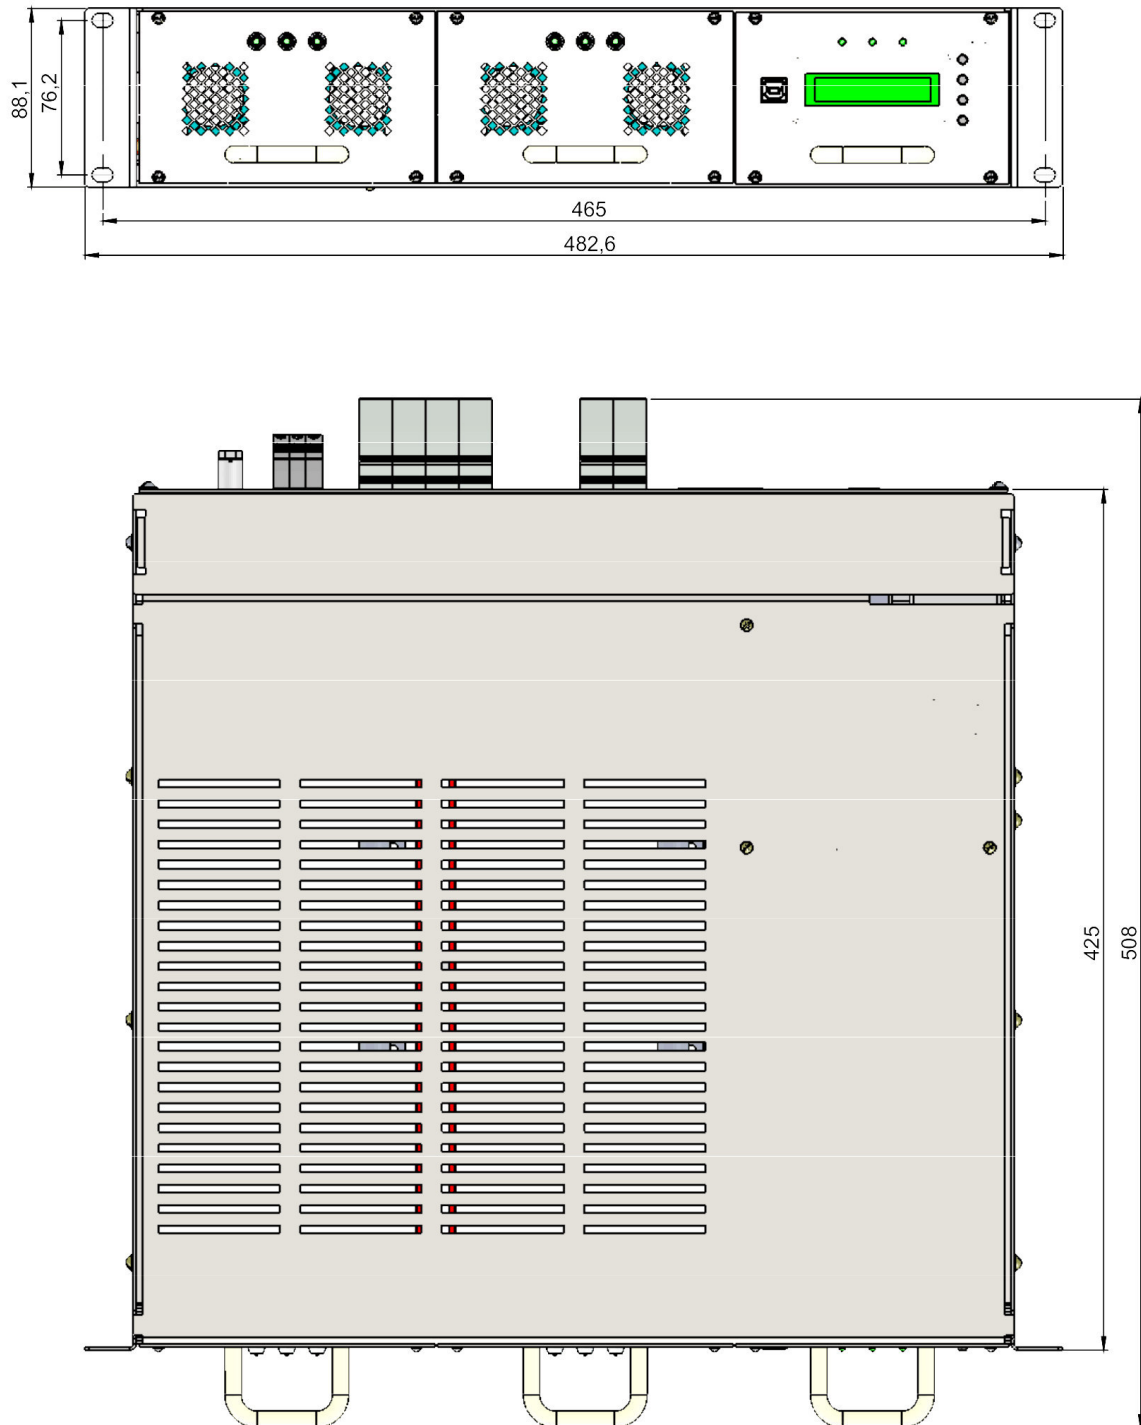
Габаритные размеры ВС24/70-2/2
